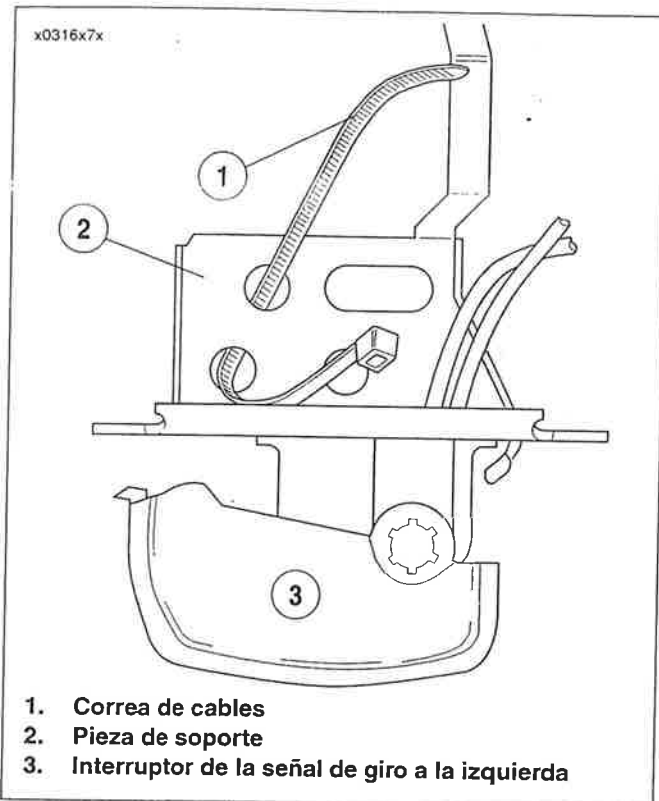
Insertar la correa de cables en la pieza de soporte del interruptor
